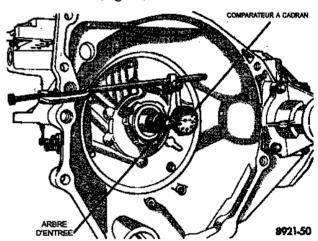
Mesure du jeu axial de l'arbre d'entrée
